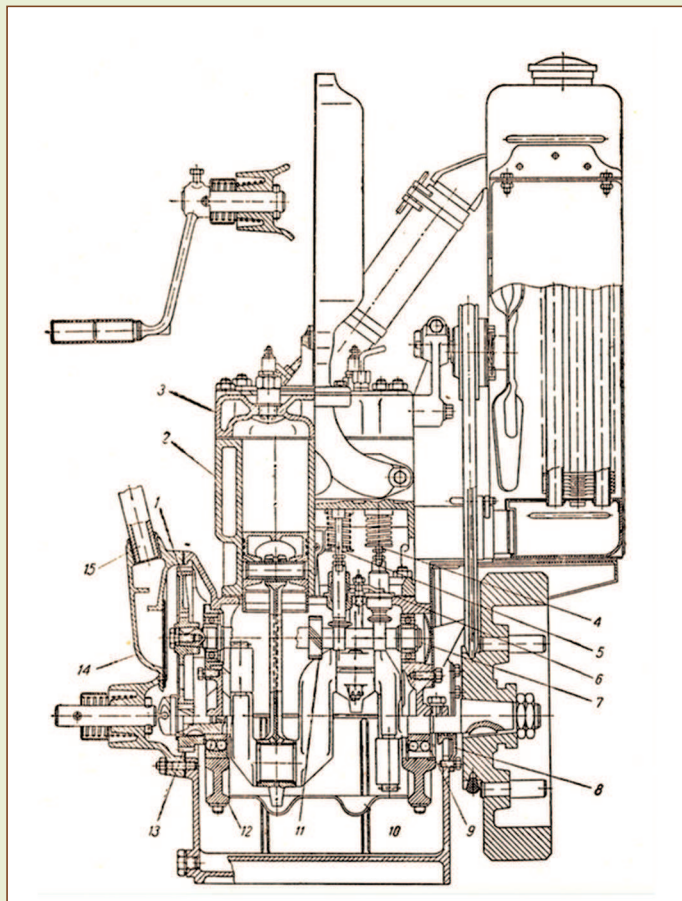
Продольный разрез двигателя Л-6/3 [4. с.31]
